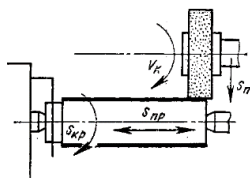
Расчетная схема продольного круглого наружного шлифования
